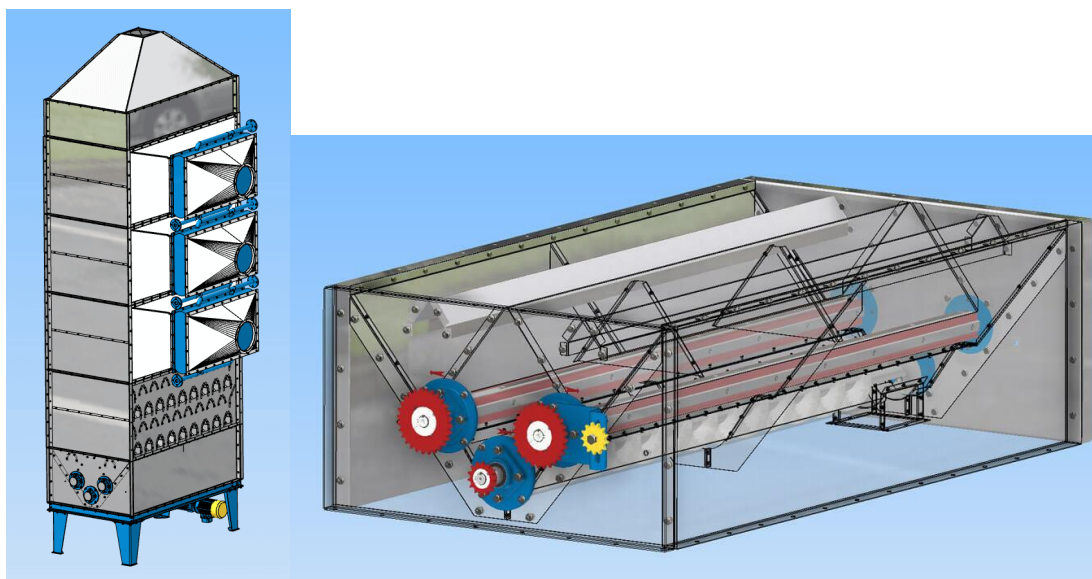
Схема шахтної сушарки СШ-3
